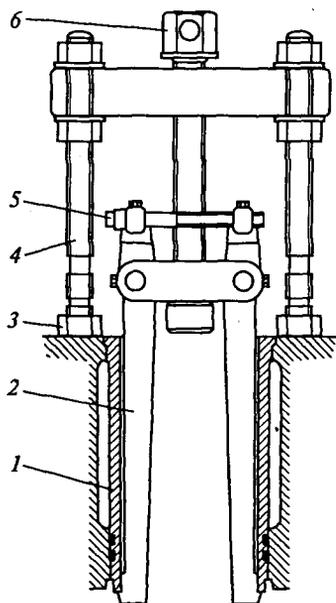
Выпрессовка гильзы из блока цилиндров комбинированным съемником: 1 — гильза; 2 — лапка; 3 — гайка; 4 — шпилька; 5 — болт; 6 — винт
